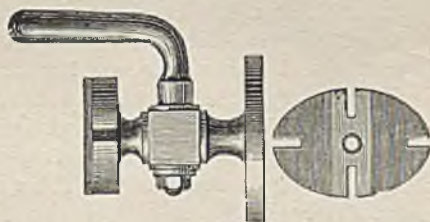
mit rundem Kontrollflansch für Bayern u. Rußland 37 mm Durchmesser, 5 mm stark;
